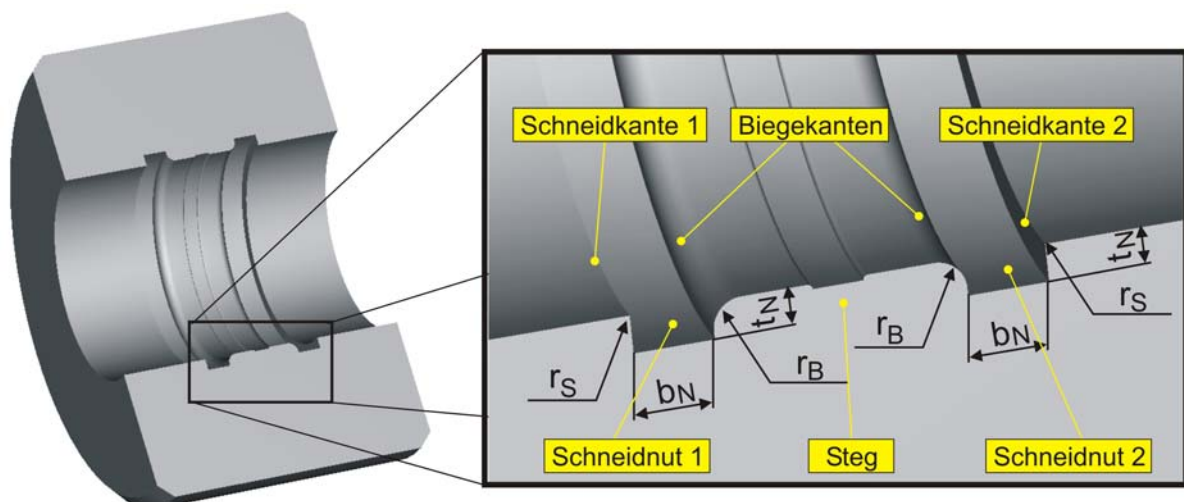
Geometrische Kenngrößen am Werkzeug für das Innenhochdruck-Doppelabschneiden
